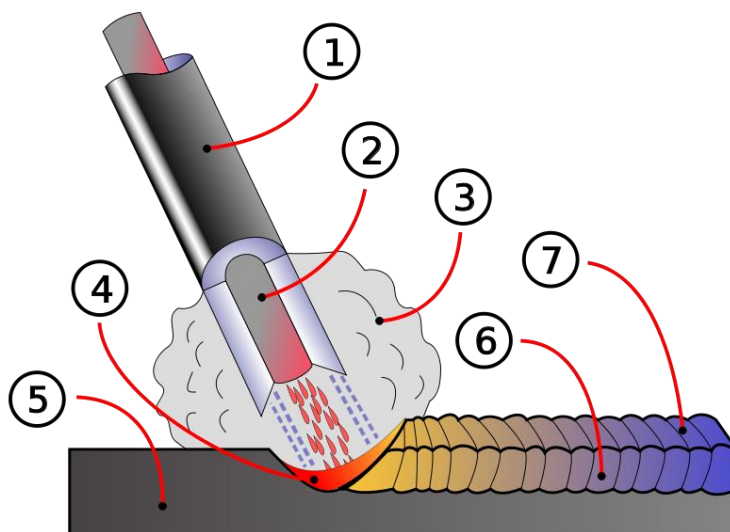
Схема ручного дугового зварювання (наплавлення) штучним електродом :
